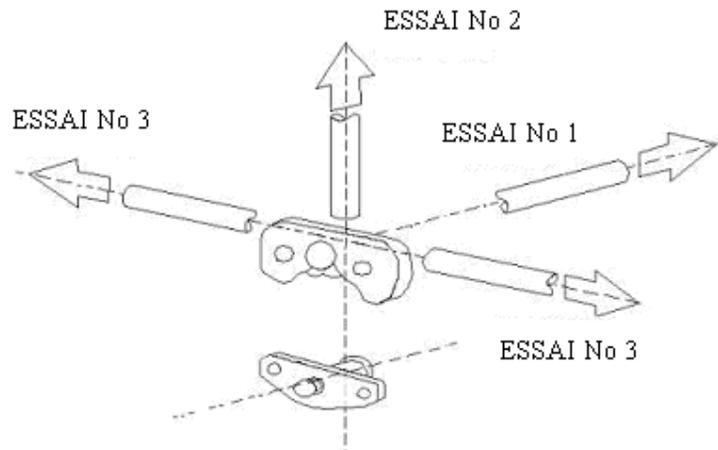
Directions d'application des forces sur la serrure de porte lors des essais statiques
